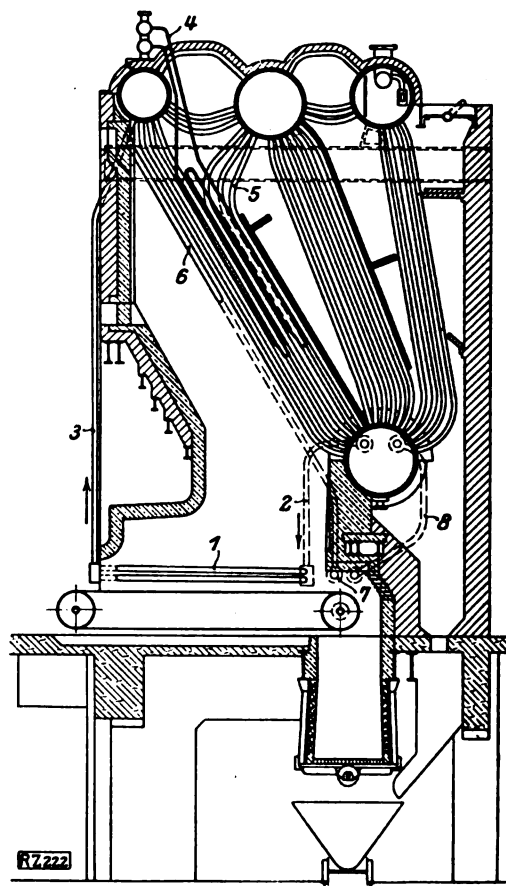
Steilrohrkessel der Heine Boiler Co.
